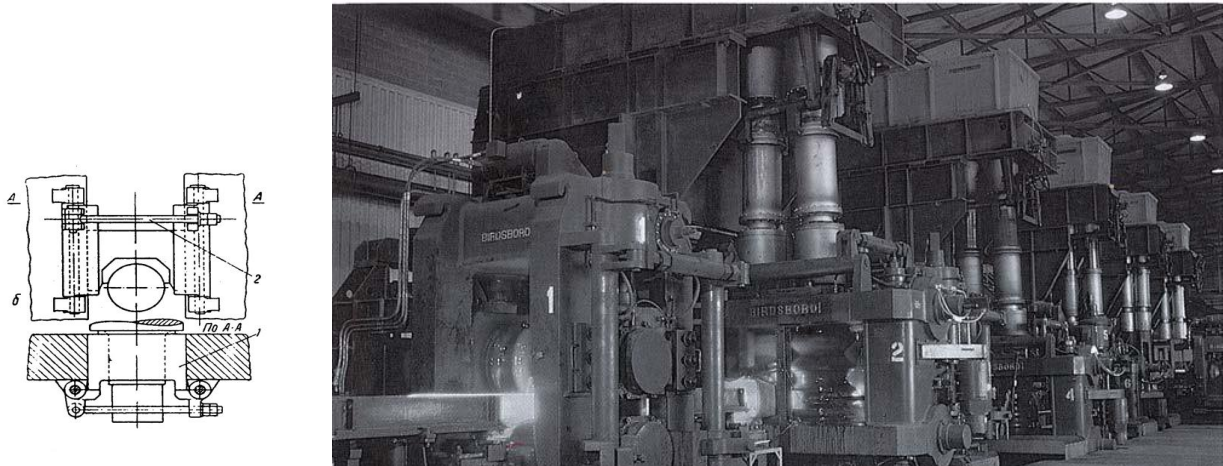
Механізм осьового регулювання зі зміщеною важільною системою та вид сортового стану, кліті якого оснащено такими механізмами [Amerigear Mill Spindles Heavy Duty, High Performance Design / Altra Industrial Motion Company. – 2012. – 20 p. - <http://www.altraliterature.com/pdfs/P-1822-AC.pdf>]
